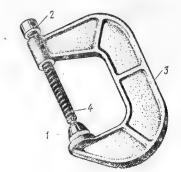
I—башмак винта; 2—головка винта; 3—скоба; 4—винт
